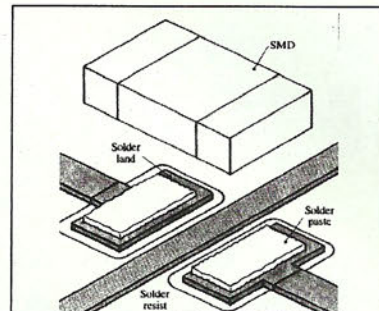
Amprentă tipică de componentă SMD cuprinzând solder land, solder rezist și solder paste
